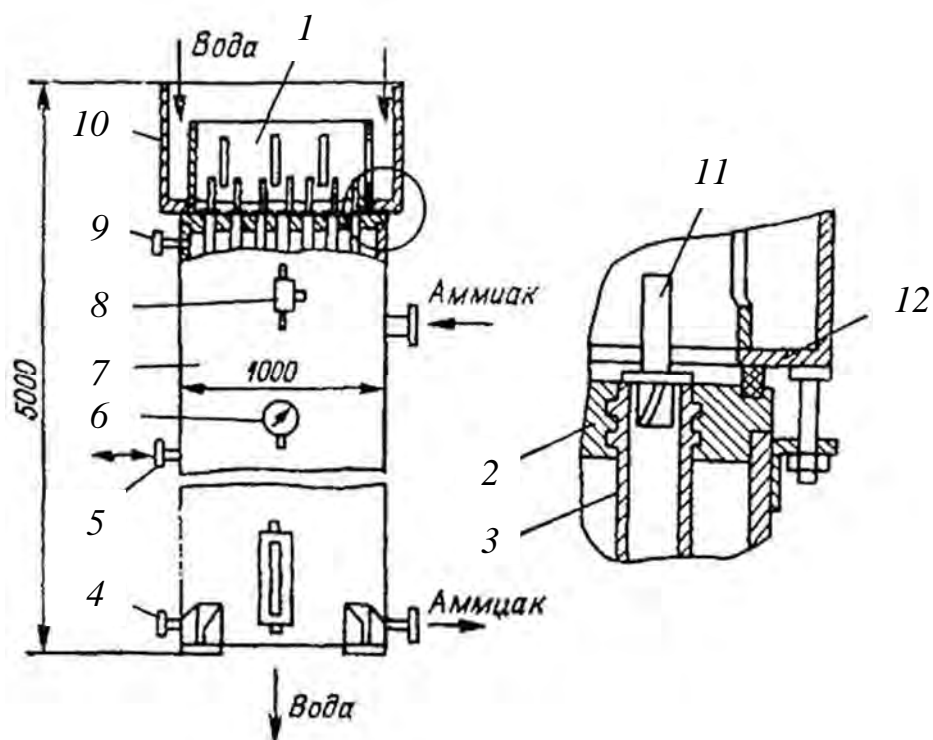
Вертикальный кожухотрубный конденсатор: 1 – цилиндрическая перегородка; 2 – трубная решетка; 3 – труба; 4 – патрубок слива масла; 5 – патрубок уравнивающей линии; 6 – манометр; 7 – корпус; 8 – предохранительный клапан; 9 – вентиль выпуска воздуха; 10 – водораспределительный бак; 11 – пластмассовая насадка; 12 – резиновая прокладка
